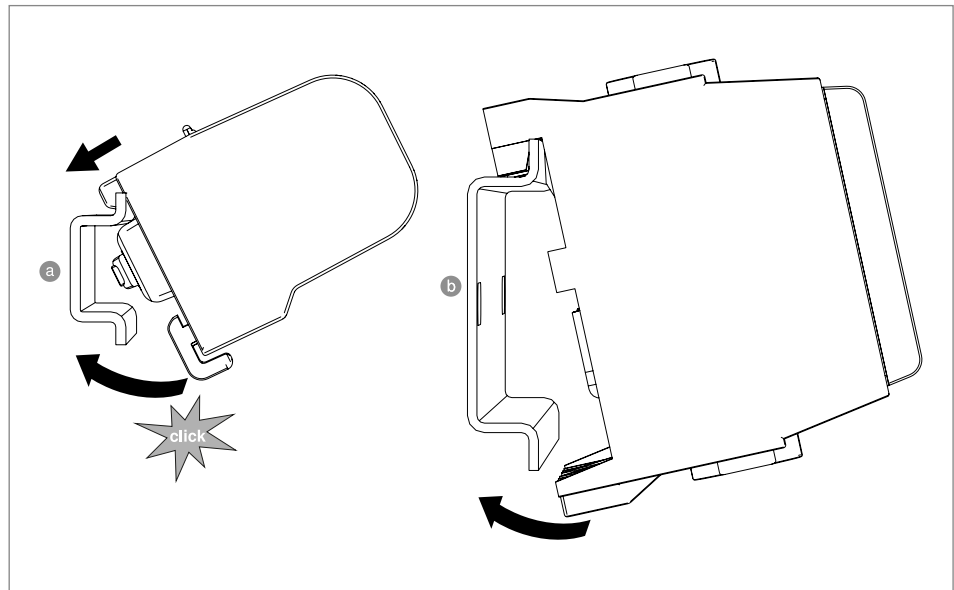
Montage d'un bornier de raccordement de type KL-T 06 sur rail DIN profilé 46277 et HLAK sur un rail DIN profilé 2069
